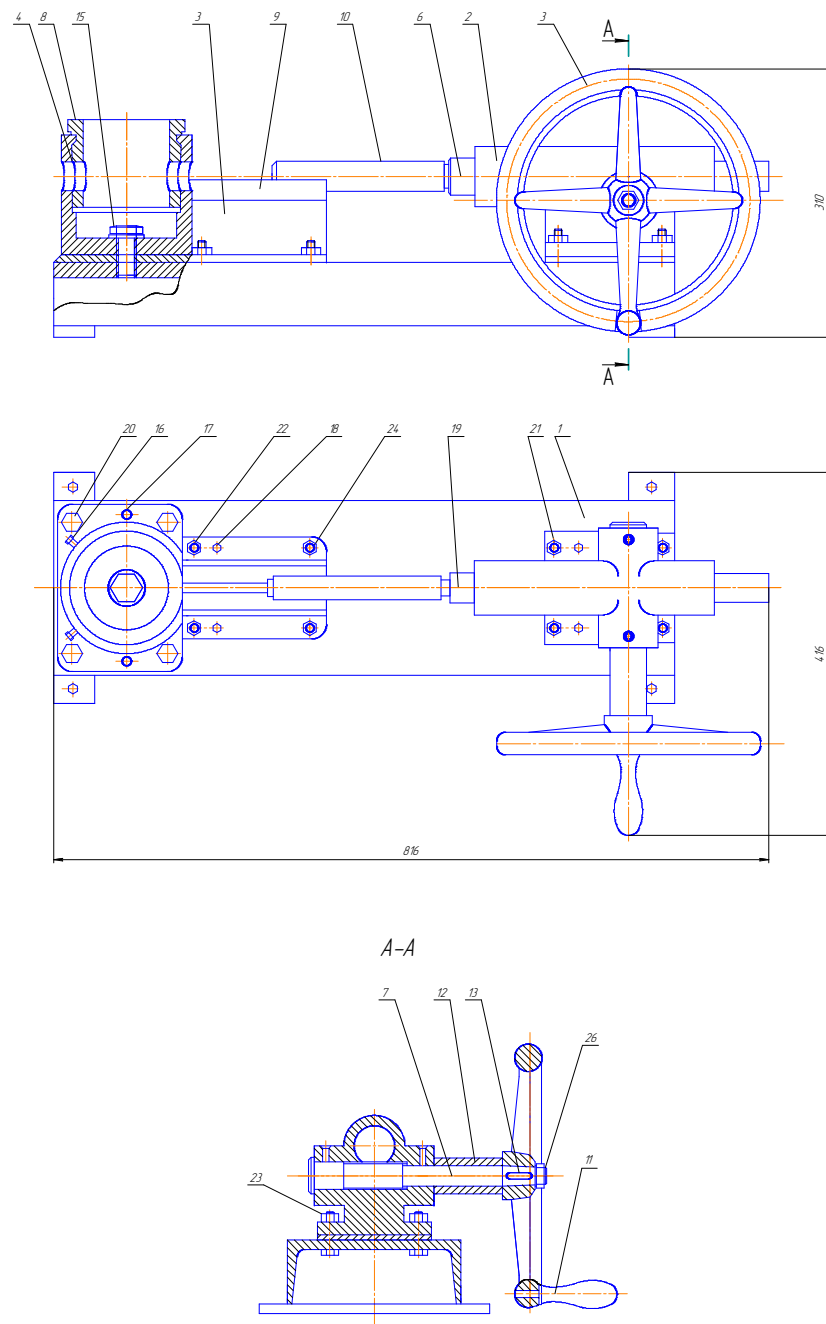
Загальний вид пристосування для збирання поршня з шатуном
